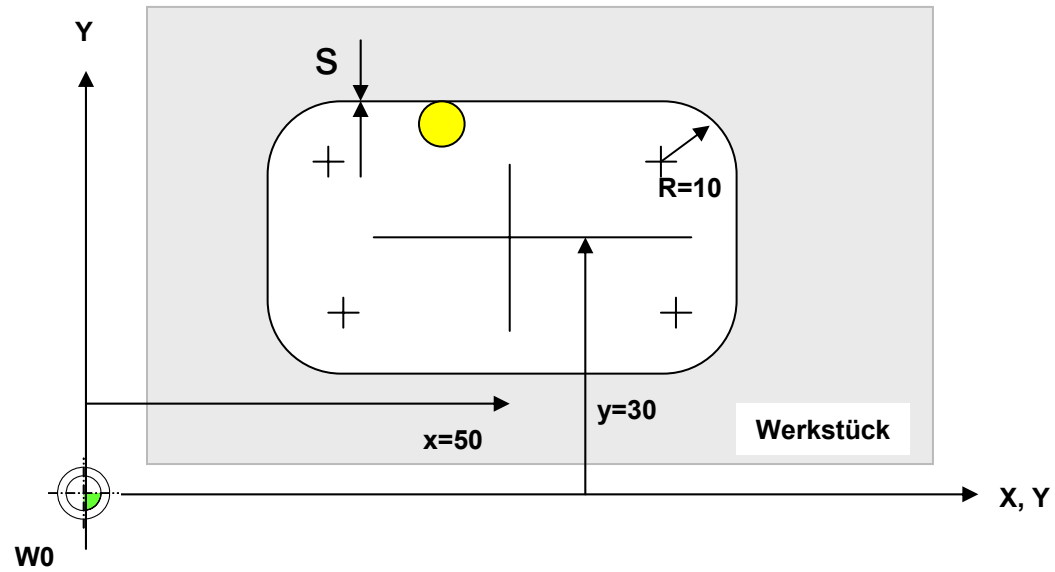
Parameter für die Definition einer rechteckigen Frästasche
